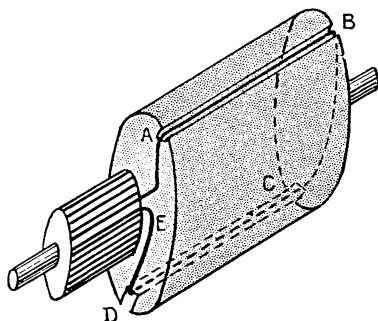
Disposition d'une section dans deux encoches de l'induit.
